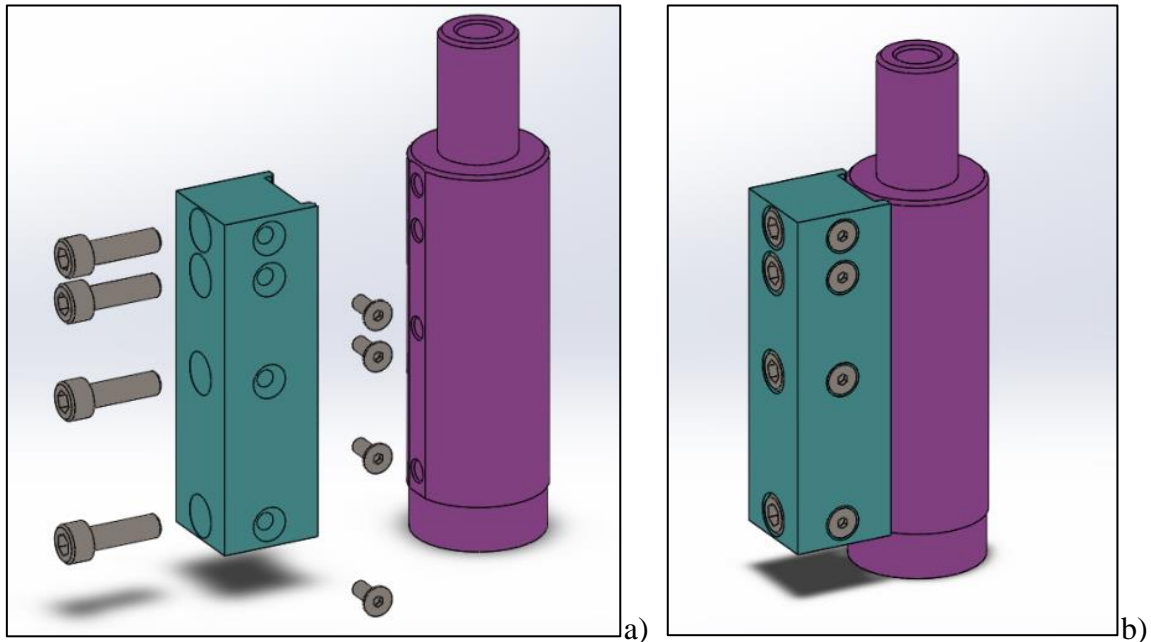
Vu en 3D du montage du support (8) sur le corps du dispositif a) Vue éclaté b) vue d'ensemble
